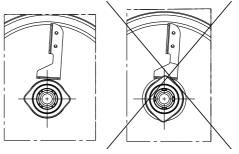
Montaje de la junta tórica en la parte fija del cierre mecánico (sólo SiC/SiC).
